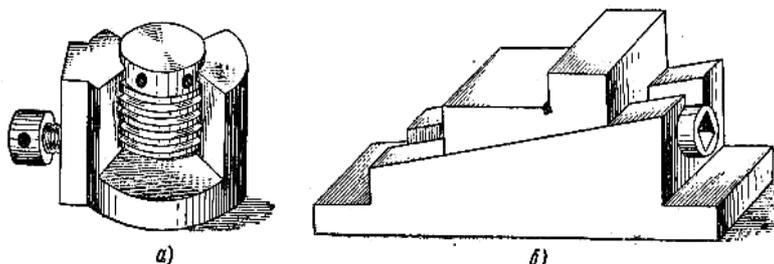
Приспособление для черновой обработки основания и направляющих
